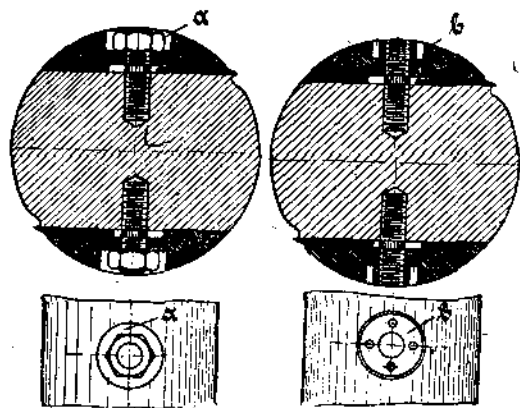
Круглый ножевой вал для комбинированных строгательных станков.
